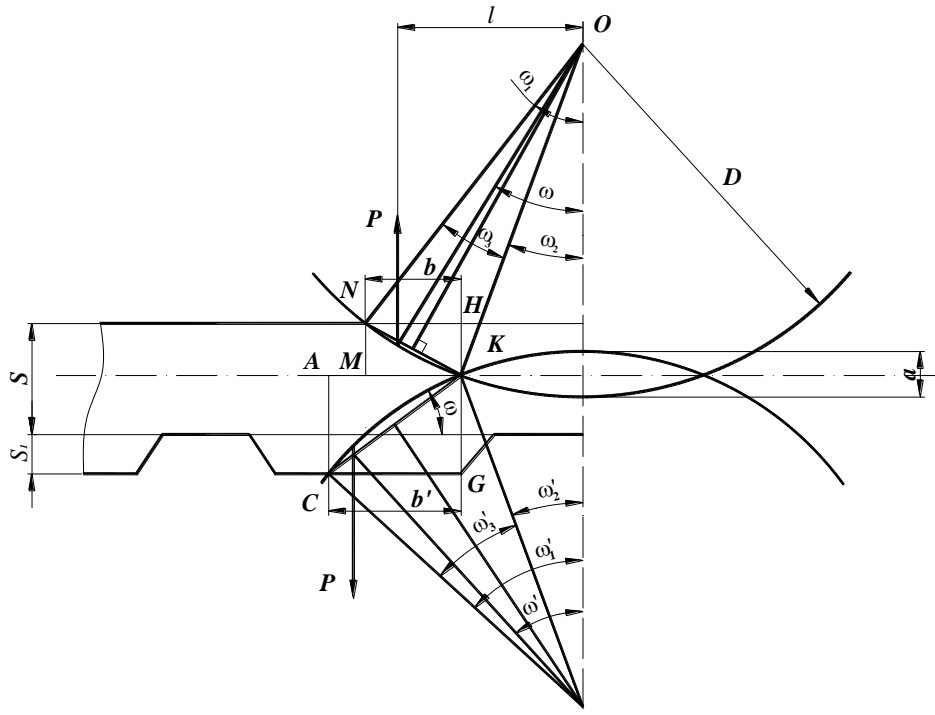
Розрахункова схема для визначення зусилля різання дисковими ножами.
